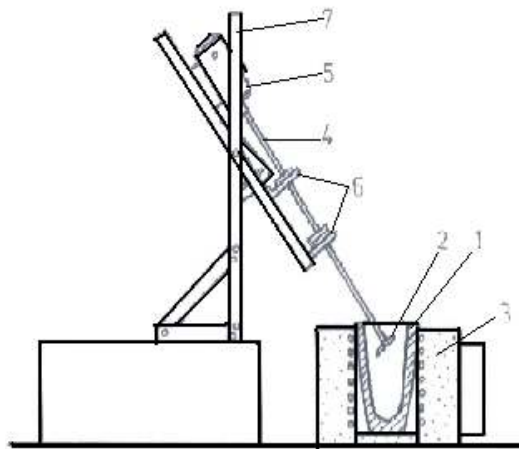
Prezentarea schematică a instalației de agitare mecanică utilizată în tehnica Vortex de dispersie a particulelor în topitură; 1- creuzet; 2- palete; 3- cuptor; 4- ax; 5- motor electric; 6- lagăre; 7- cadru de sprijin.
